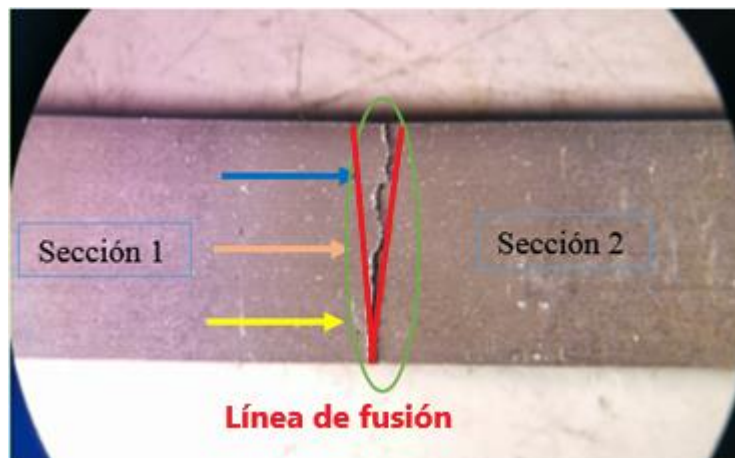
Fotografía de la probeta fracturada por el ensayo de tracción.
